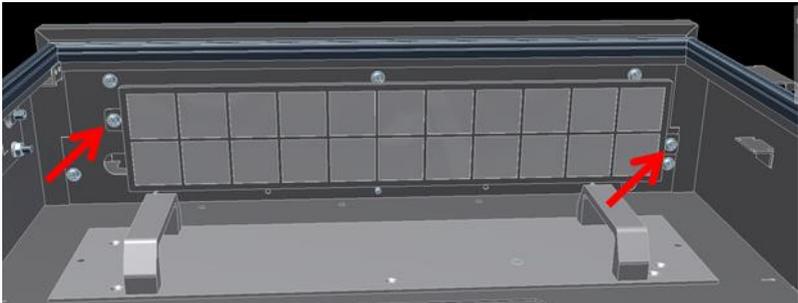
smontaggio e sostituzione del filtro dell'aria – vista anteriore dal basso
